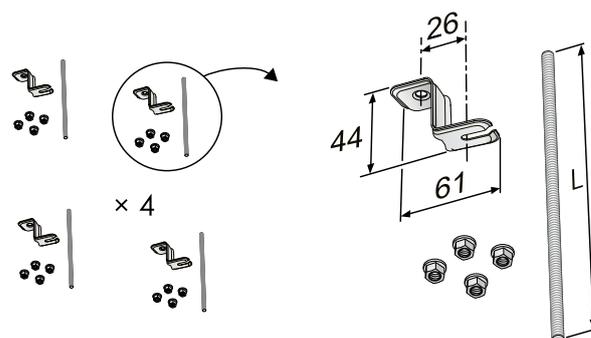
Élément d'assemblage SYST MS M8-1, montage au plafond et sur tige filetée
